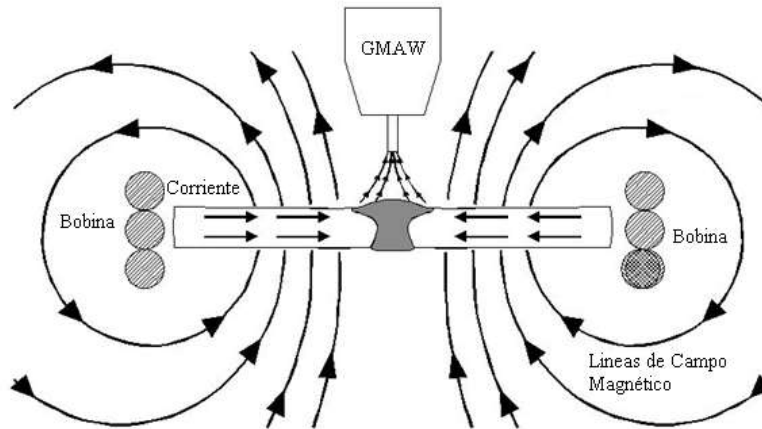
Ilustra la forma de aplicar el campo magnético externo durante la soldadura y la interacción con el campo magnético generado por la corriente de soldadura.
